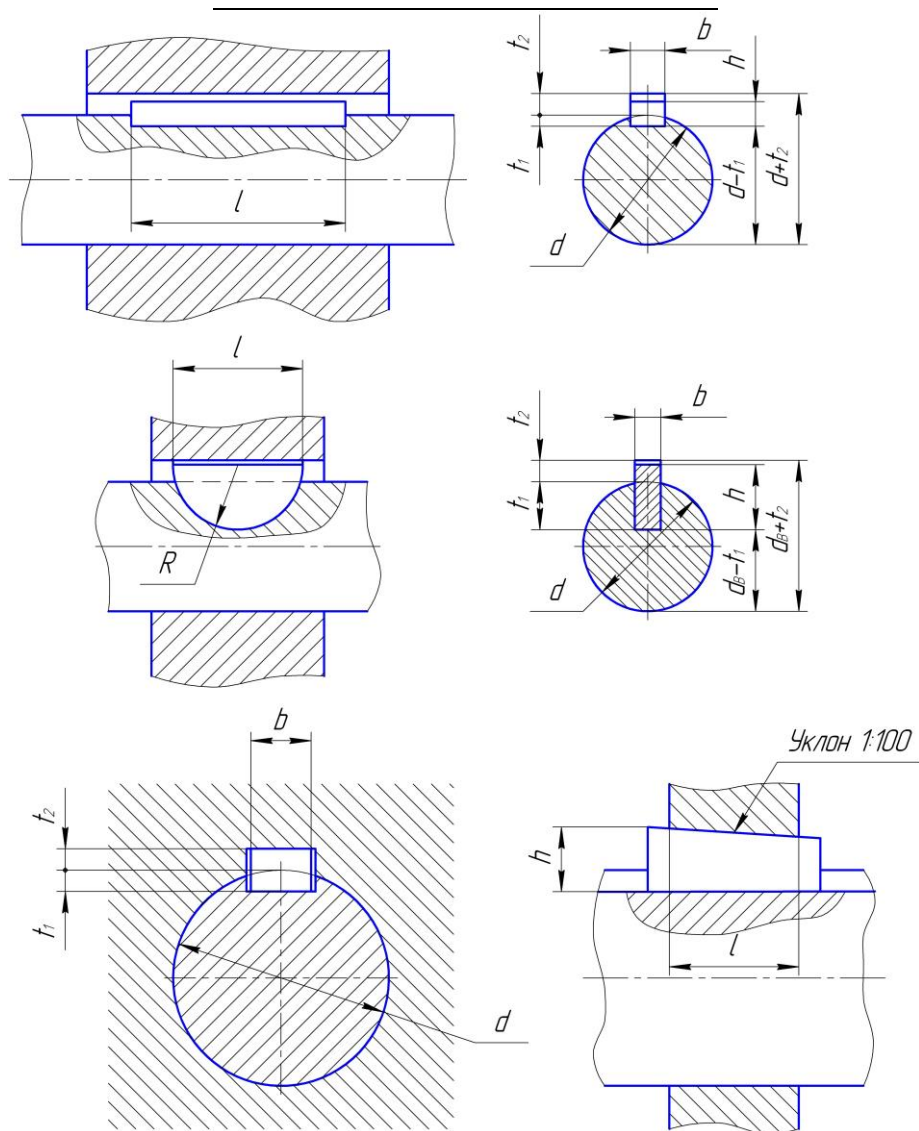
Шпонкове з'єднання маточин коліс з валами
